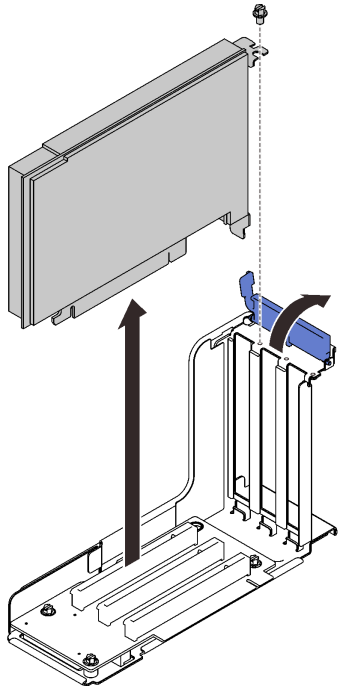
Removendo um adaptador do conjunto da placa riser PCIe
